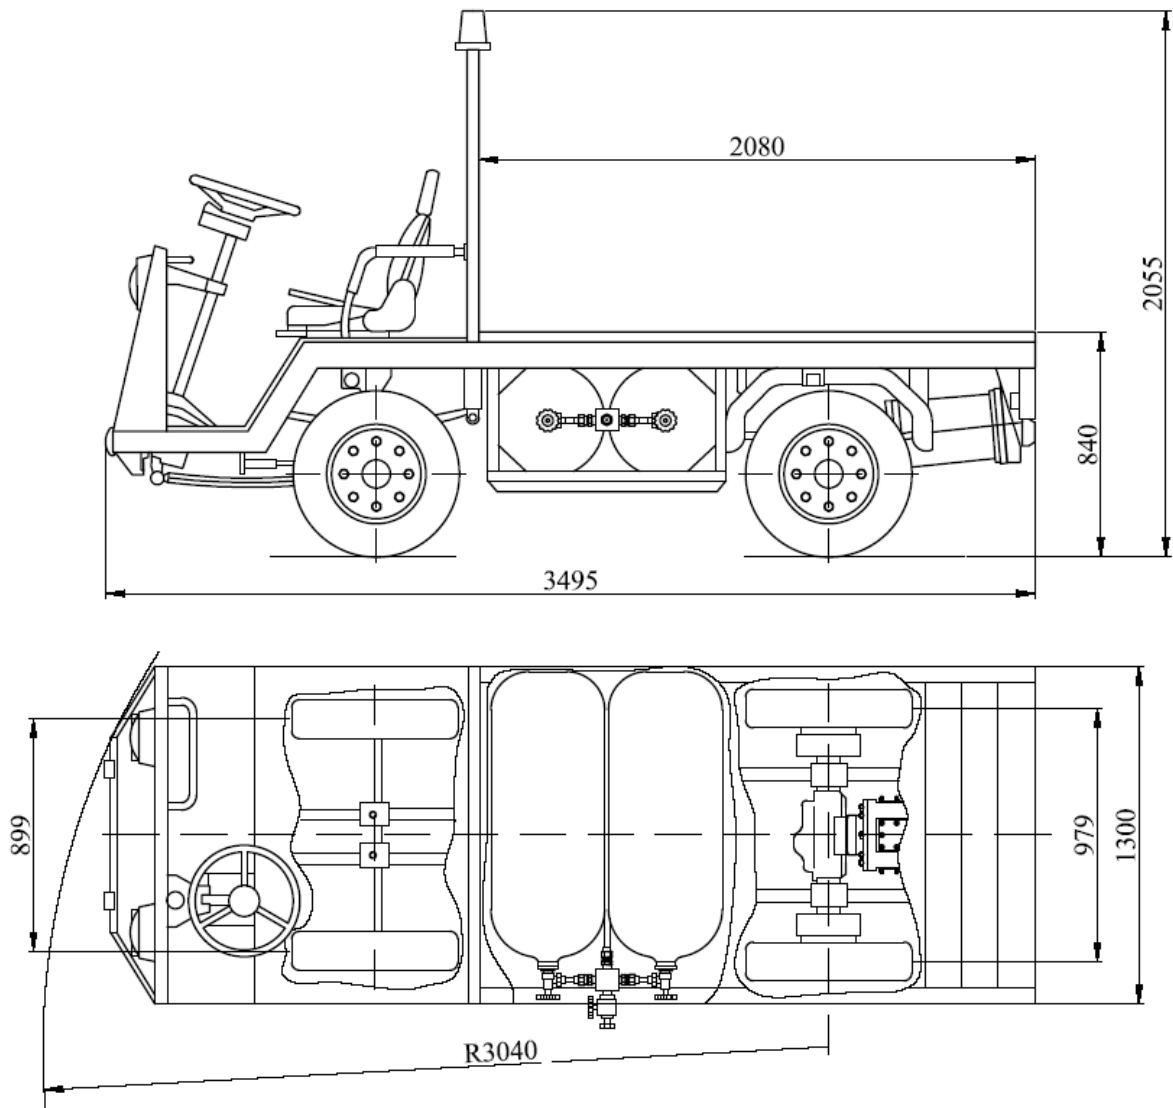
Схема платформного візка з пневматичним приводом на базі роторно-поршневого двигуна об'ємної дії із шарнірно-кулачковим механізмом руху
